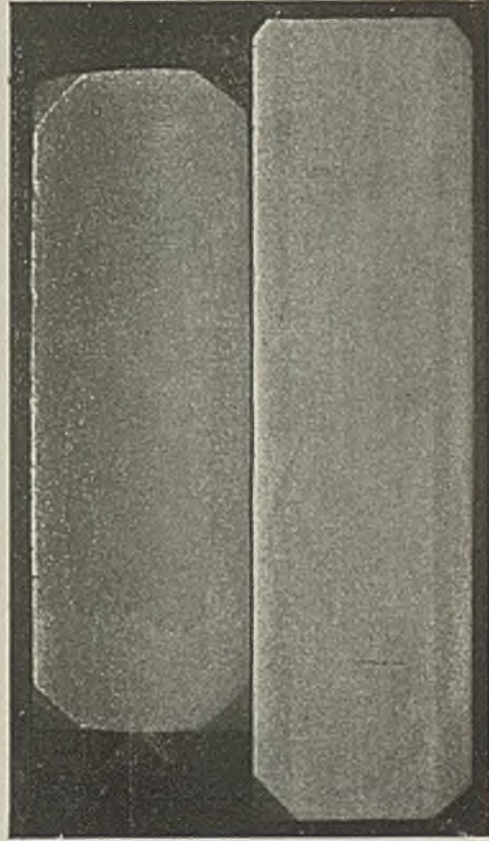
Oben Querschnitt, unten Längsschnitt.
